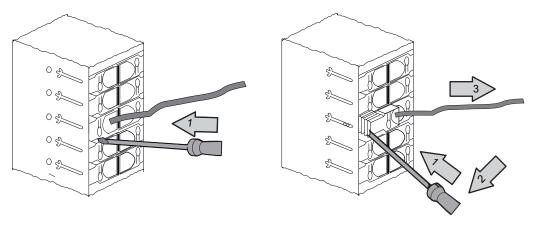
Déconnexion d'un câblage d'un connecteur Fast Connect à 40 points
